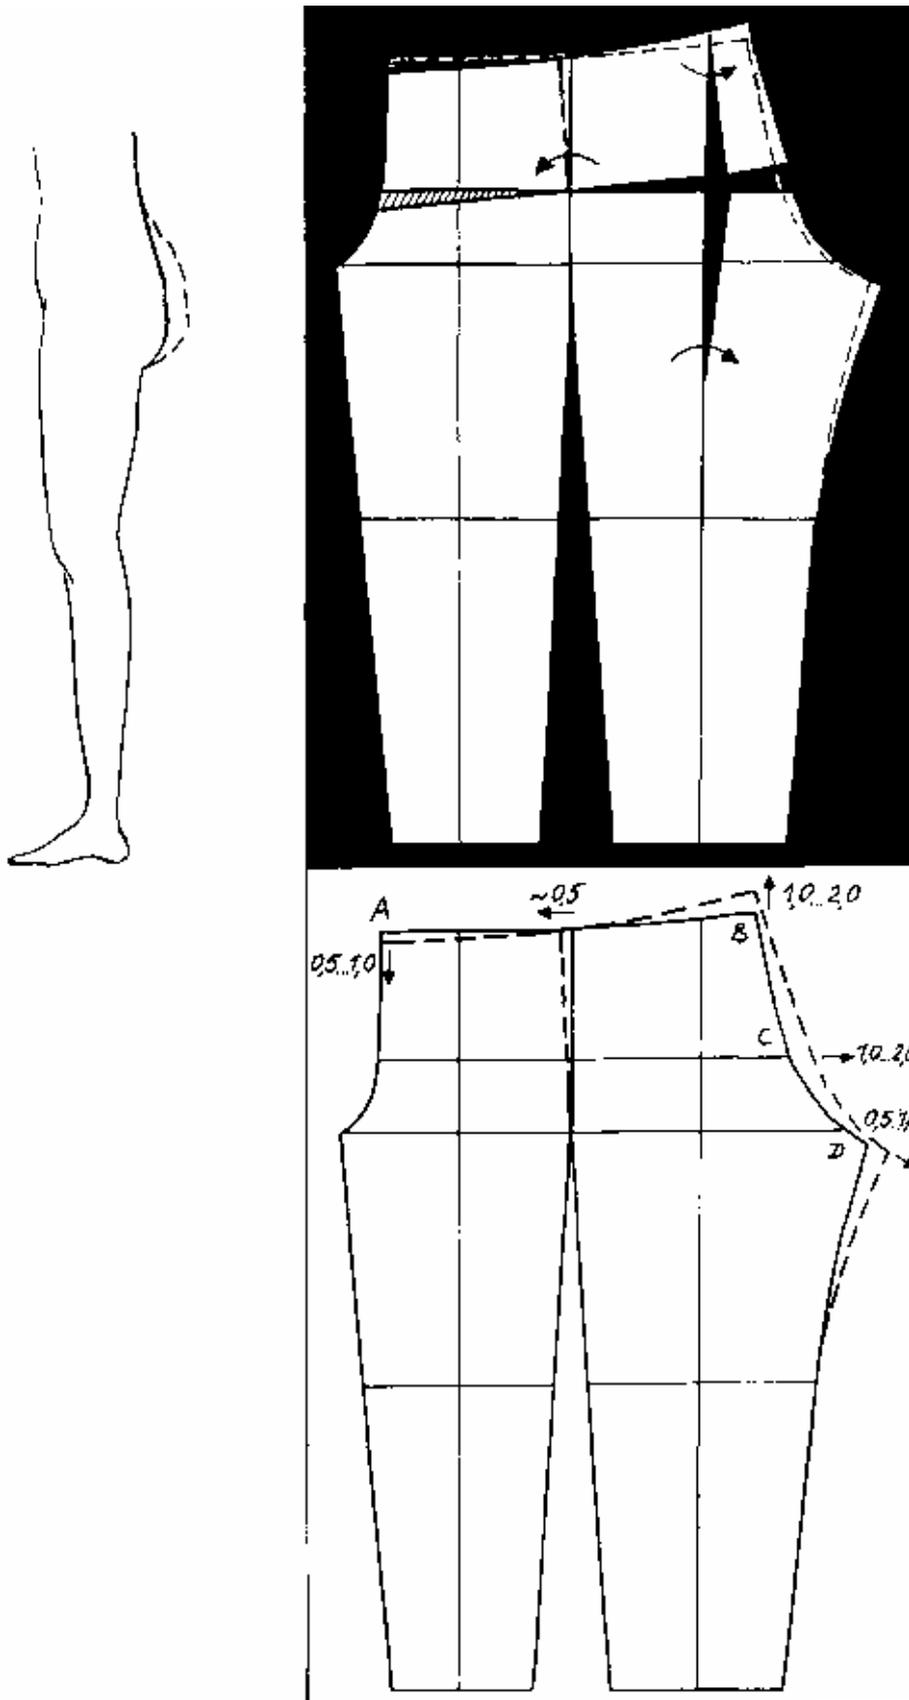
Корректировка чертежа конструкции на фигуру с выступающими ягодицами
